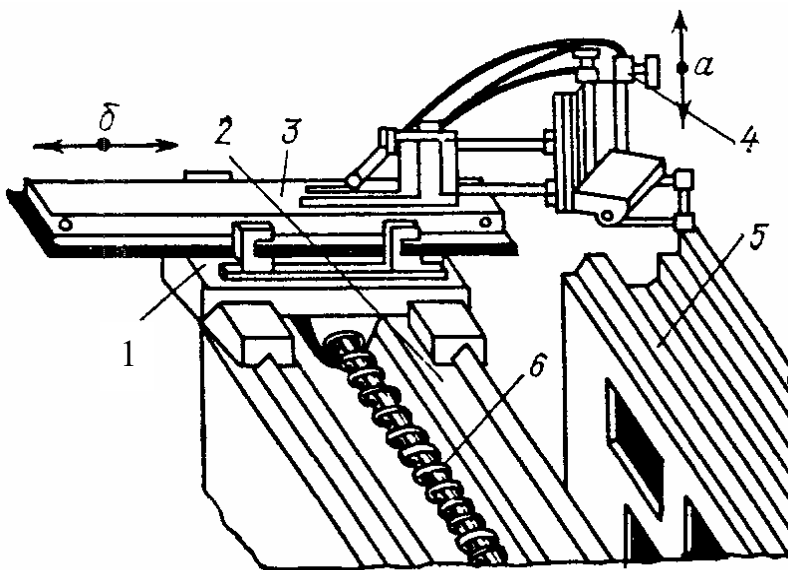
Стенд для газополум'яного гартування напрямних
